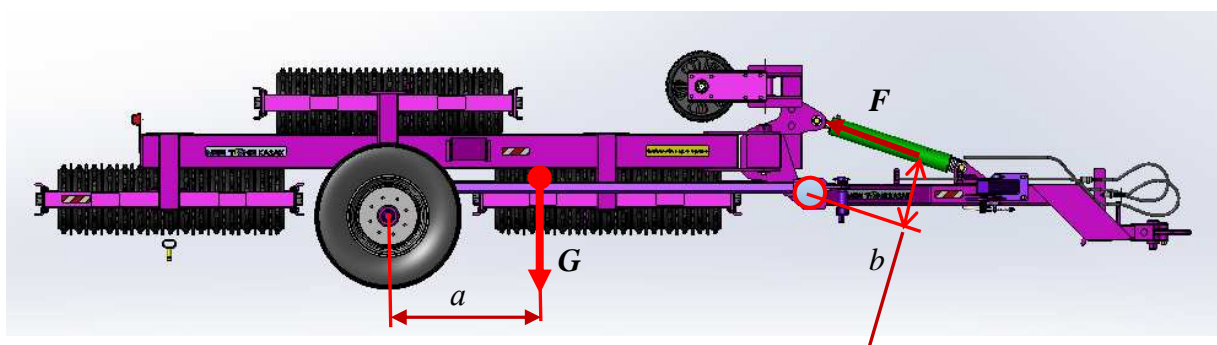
Расчетная схема для определения усилия на штоке гидроцилиндра катка прикатывающего зубчато-кольчатого КЗК-12 «Казак»
